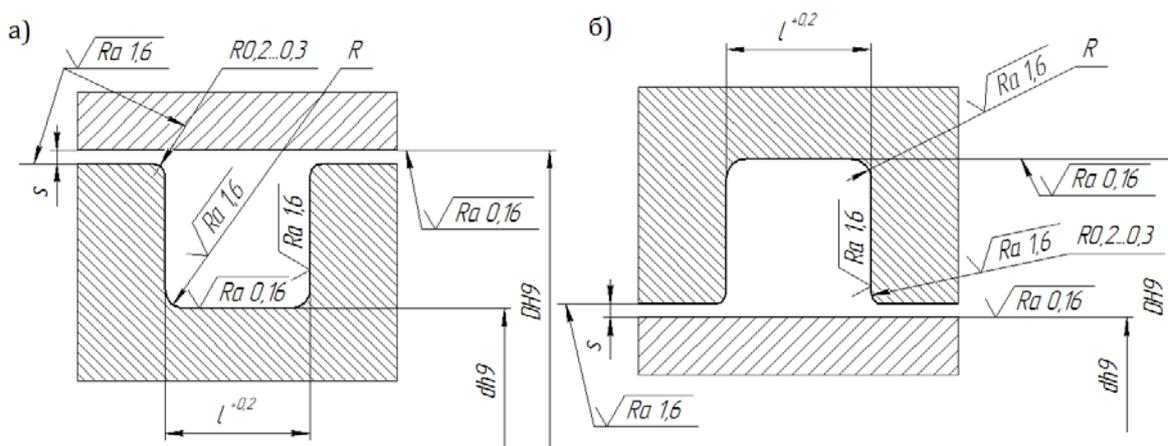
Канавки под уплотнение: а – поршня, б – штока
